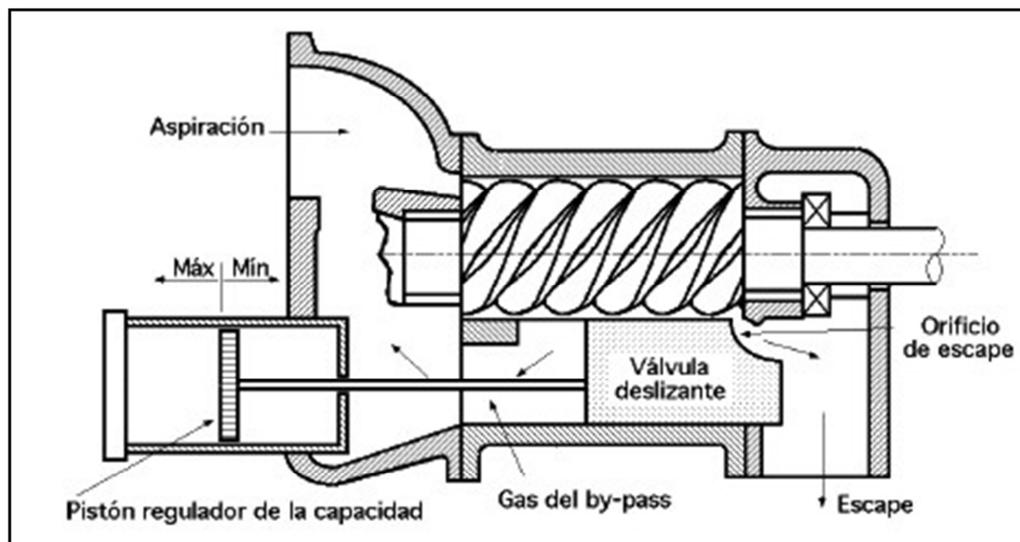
ESQUEMA COMPRESOR DE TORNILLO Y DISPOSICIÓN DEL TORNILLO COMPRESOR
